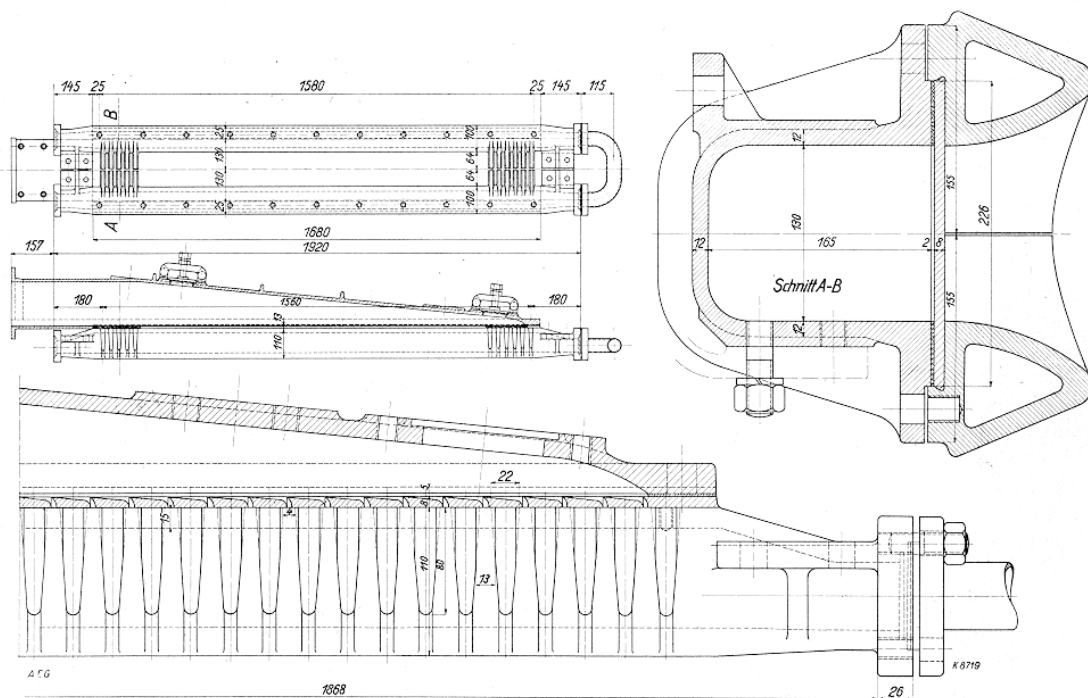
Neue Schlitzdüse mit Kühlkörper.
